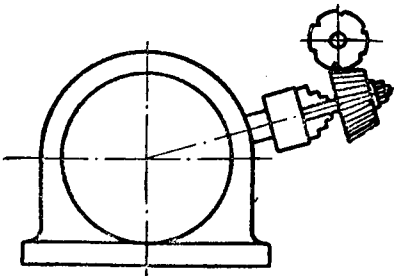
Разжимная оправка для крепления фрикционного конуса при фрезеровании
